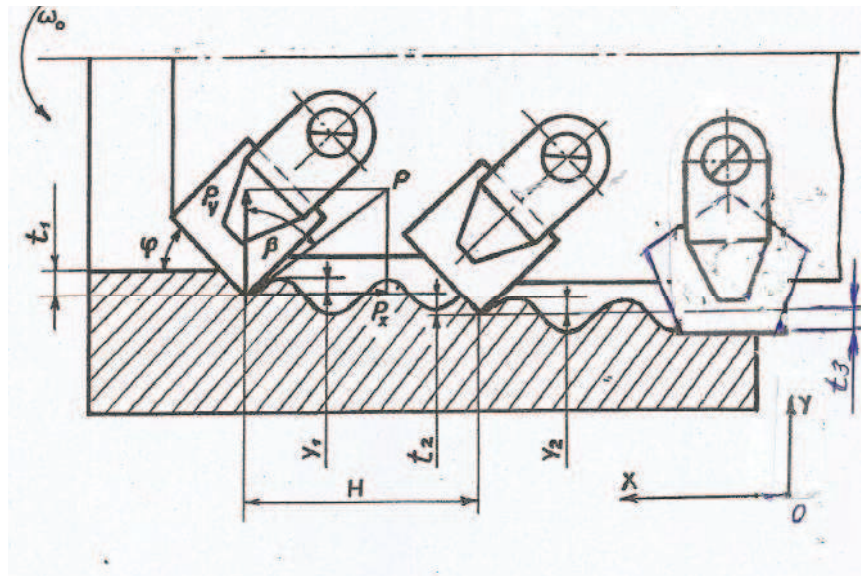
Схема фрезы со сменными твердосплавными пластинами при взаимодействии на нее автоколебаний в процессе деления припуска
